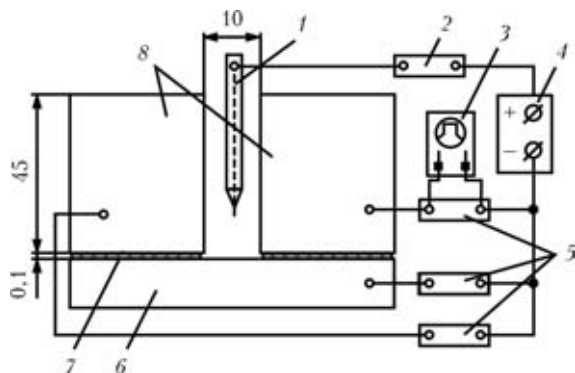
Схема установки для измерения тока, протекающего через боковые стенки разделки при СУЗ с управляющим магнитным полем: 1 — вольфрамовый электрод; 2 — шунт для измерения сварочного тока; 3 — осциллограф; 4 — источник питания; 5 — шунты для измерения тока, протекающего через боковые и нижнюю стенки; 6 — нижняя стенка разделки; 7 — изолятор; 8 — боковые стенки
